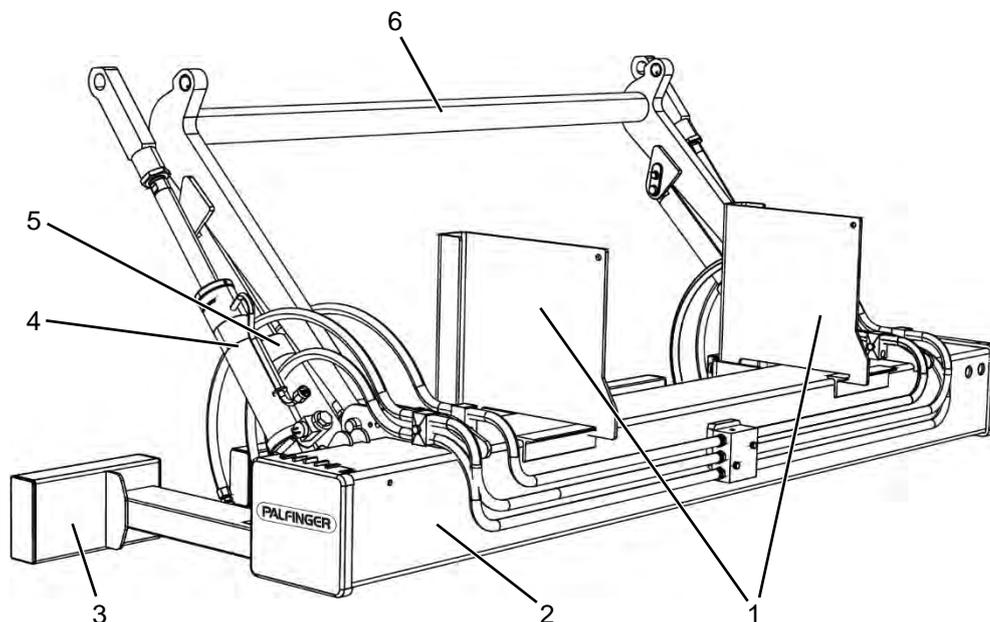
Подъемно-погрузочная платформа с консолями с резьбовыми соединениями и вставным агрегатом
